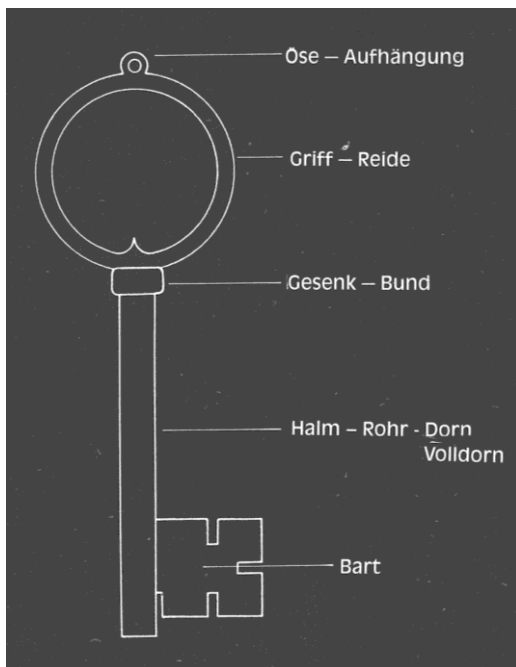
Bartschlüssel-Begriffsklä rung; Abbildung - Gabriel Mandel
